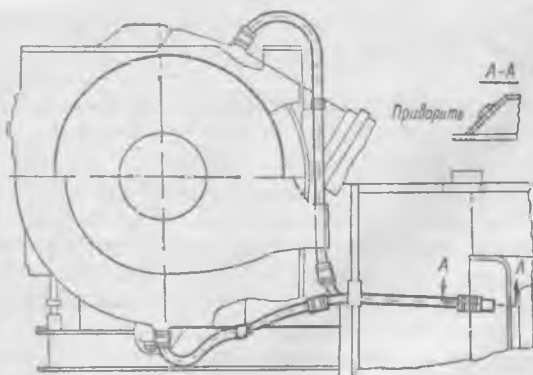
Расположение труб, подводящих воздух из ресивера к лабиринтовому уплотнению подшипника турбовоздуховки
